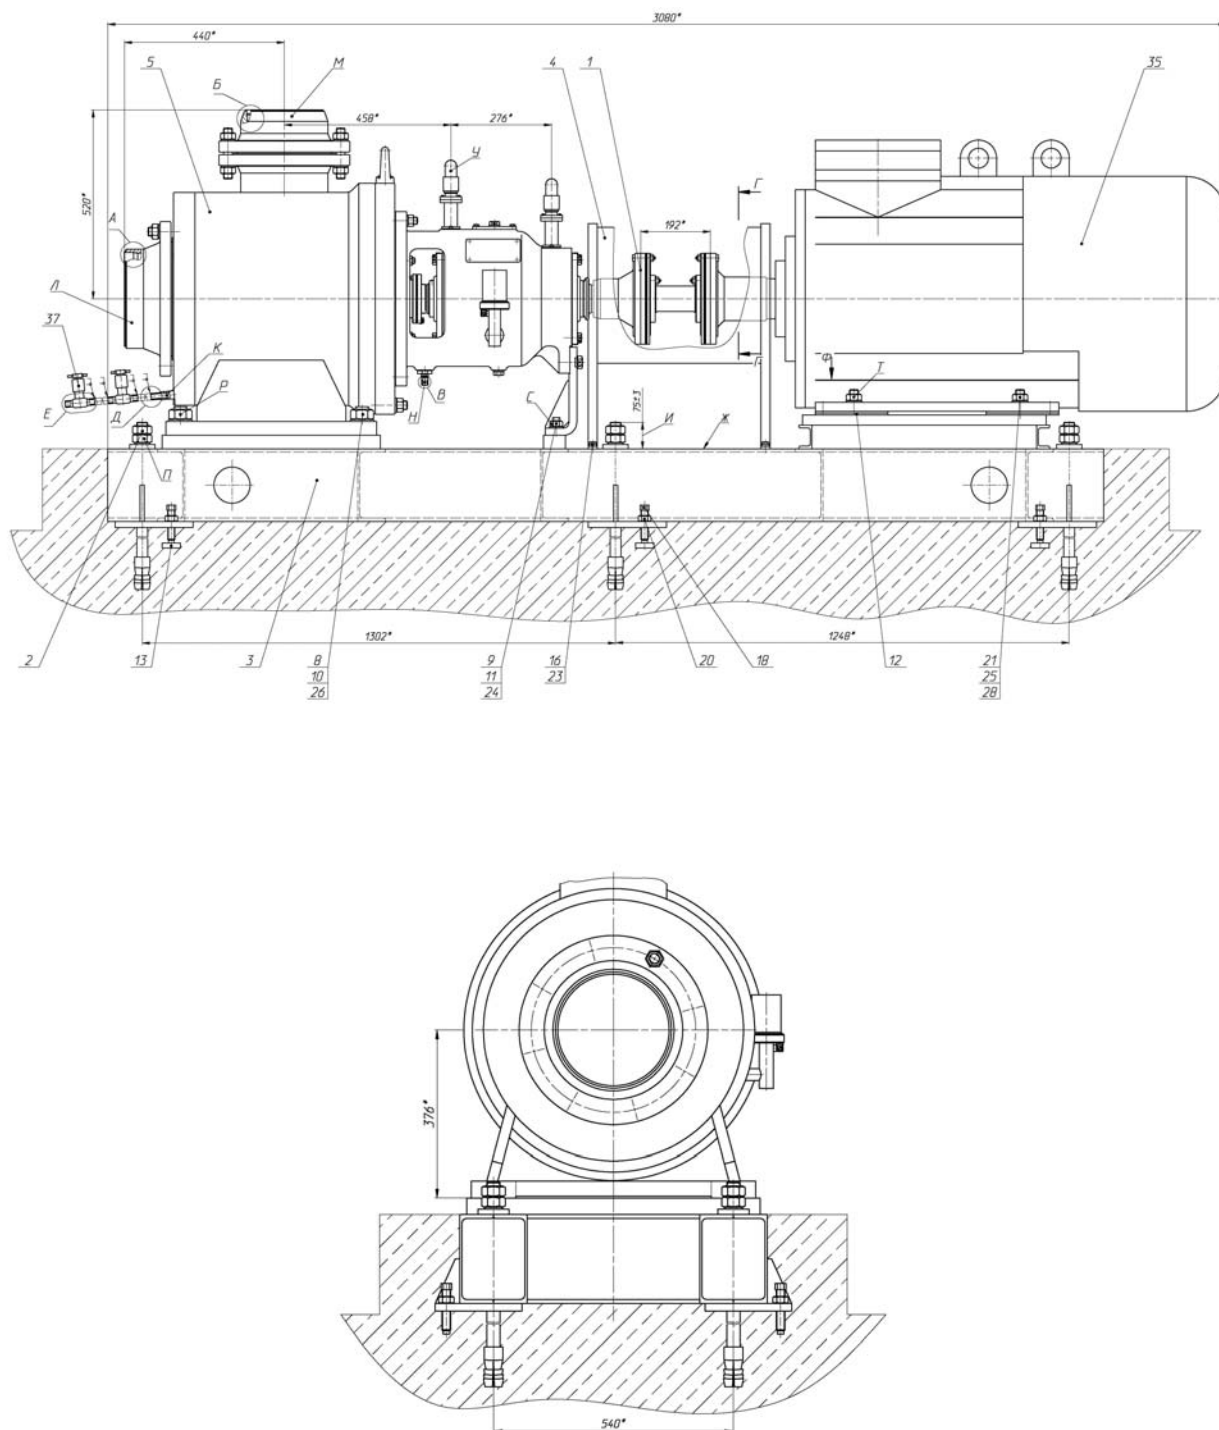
Габаритный чертеж спринклерного насоса
